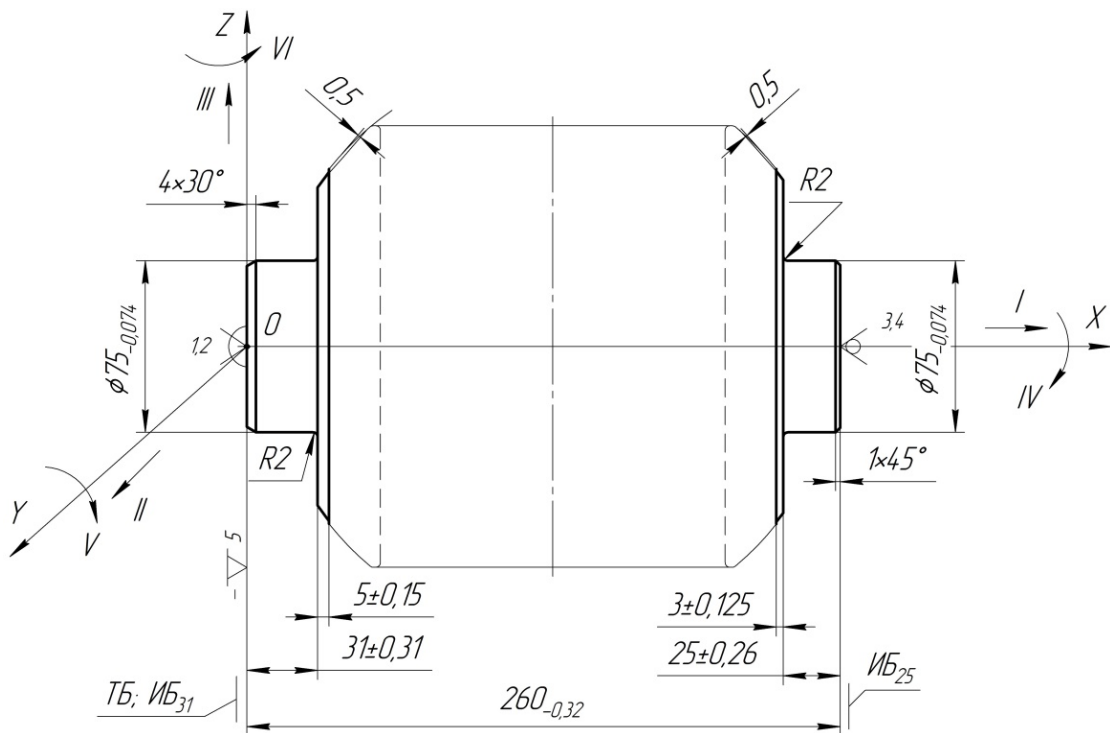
Базування заготовки на операції 035. Схема №2
